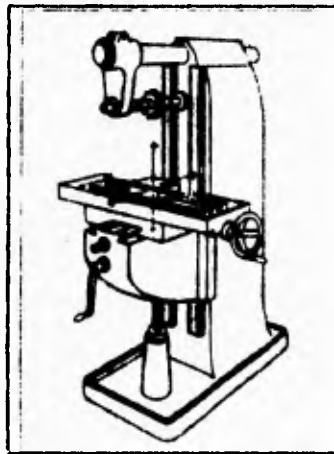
Fresadora horizontal con los movimientos que puede realizar.
